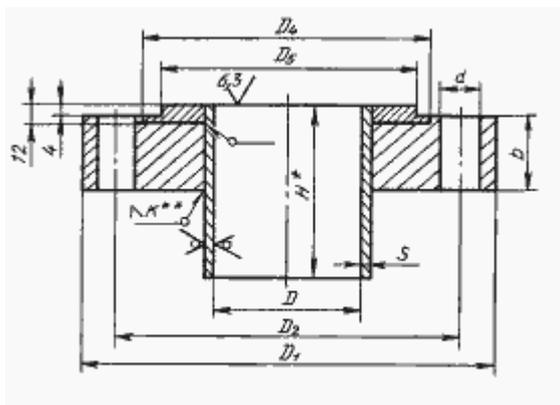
Стальной плоский приварной фланец с выступом, наплавленным коррозионно-стойкой сталью.
